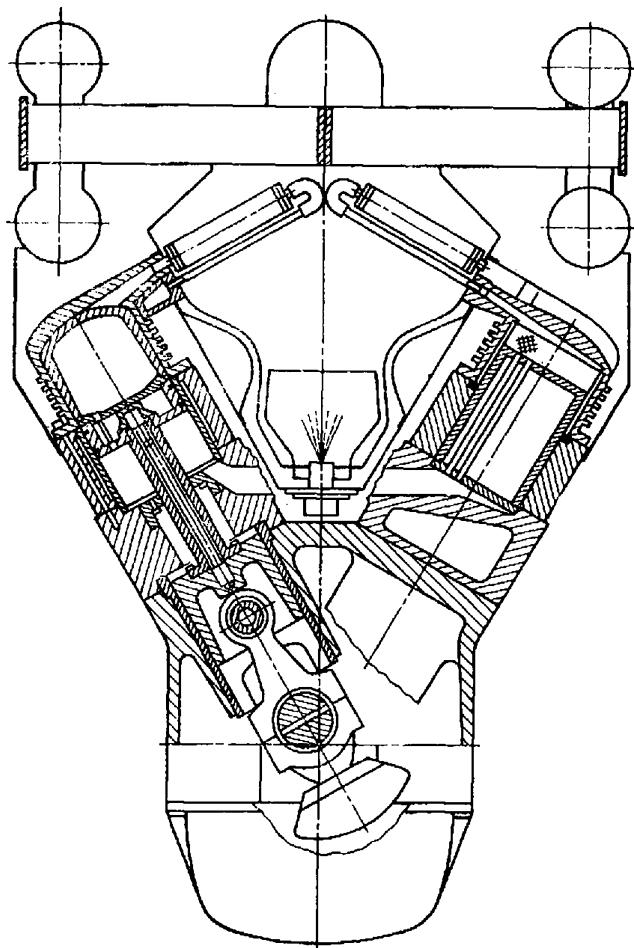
Схемы соединения цилиндров и расположения кривошипов в шестицилиндровом двигателе Стирлинга двойного действия * [390]
